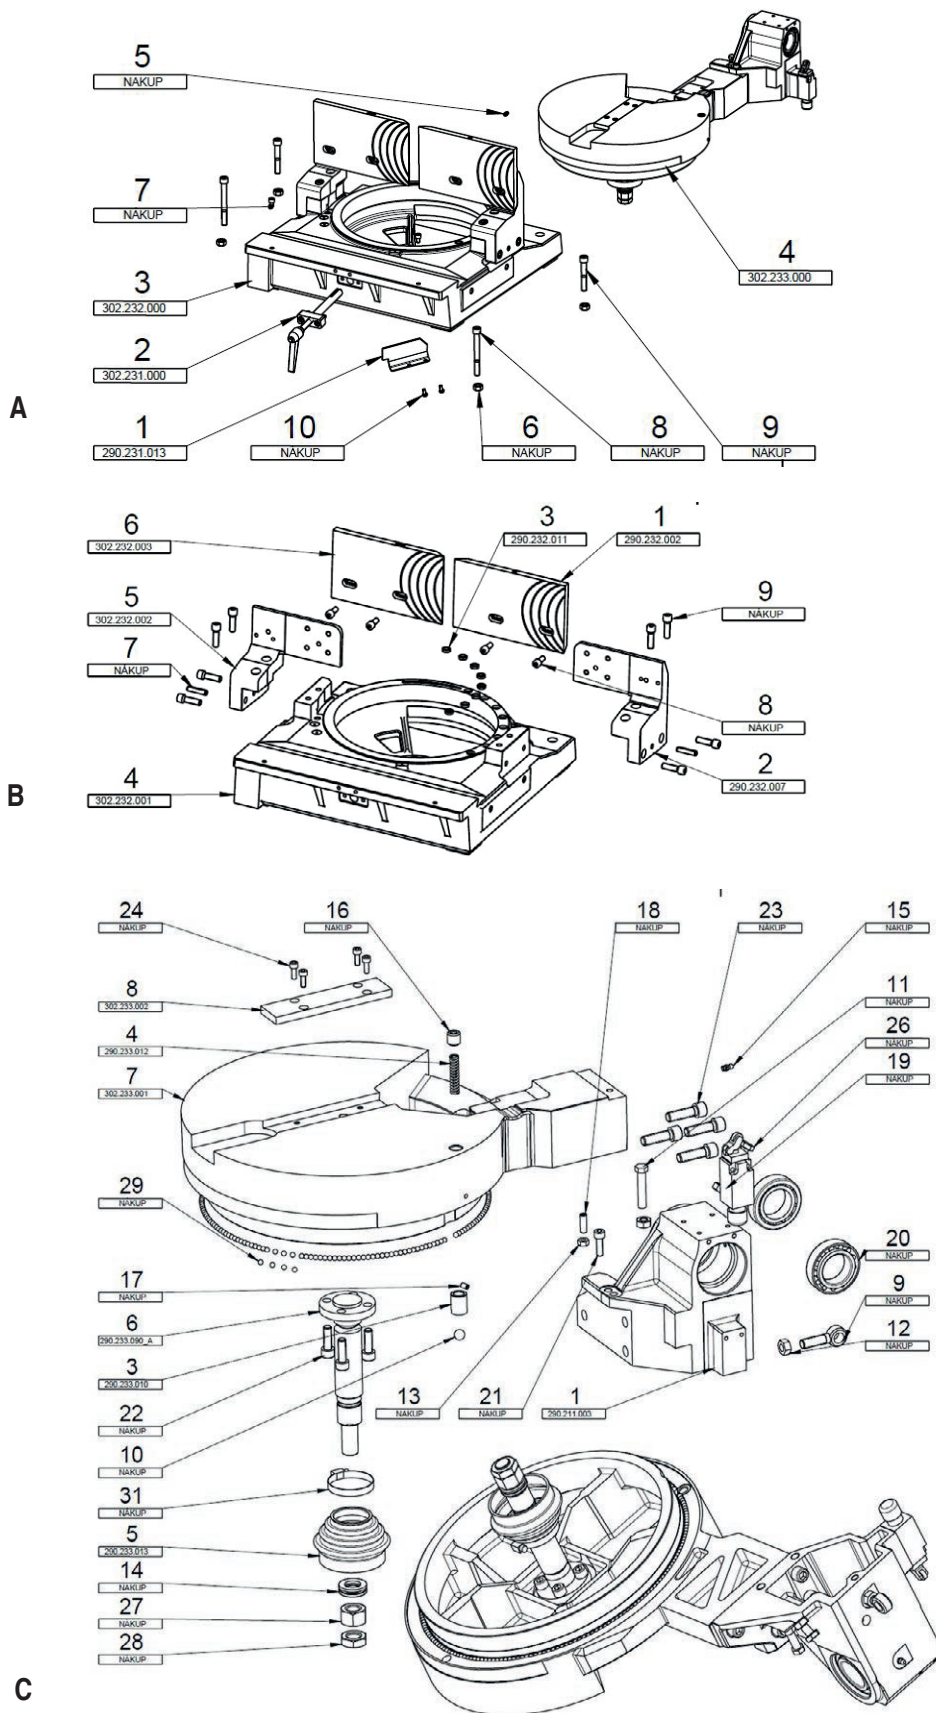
Onderdelentekening 8 A, B, C : Draaitafel en spanklembek
